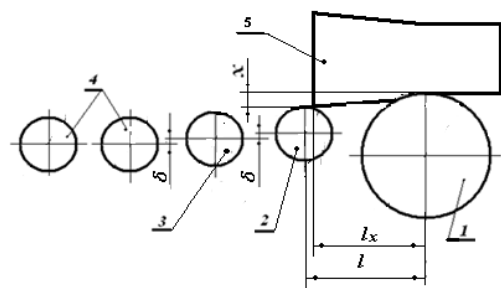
Схема установки нижнього робочого валка та робочих і станинних рольгангів на блюмінгу: 1 - нижній робочий валок; 2 - перший станинний ролик; 3 - другий станинний ролик; 4 - робочий рольганг
